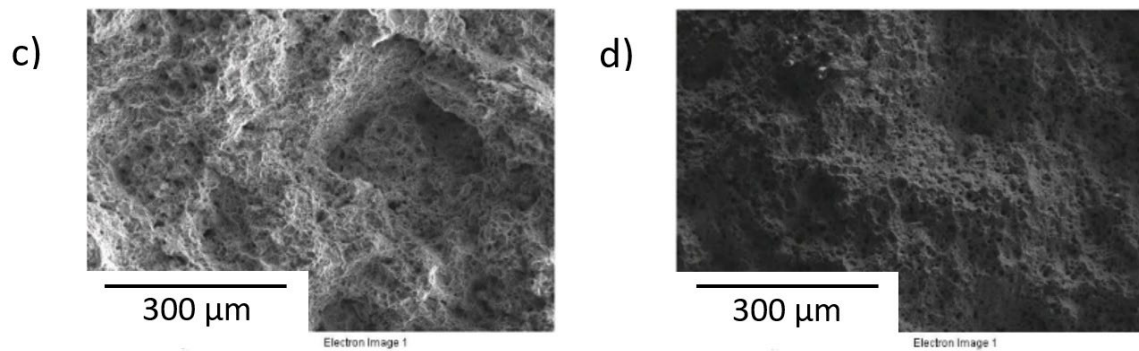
Superficie di frattura del provino in CW625N a cuore c) prima e d) dopo ricottura a 530°C per 2h (Raff. 40°C/h) / Fracture surface of the CW625N specimen in the core c) before and d) after annealing at 530°C for 2h (Cooling Rate 40°C/h).
